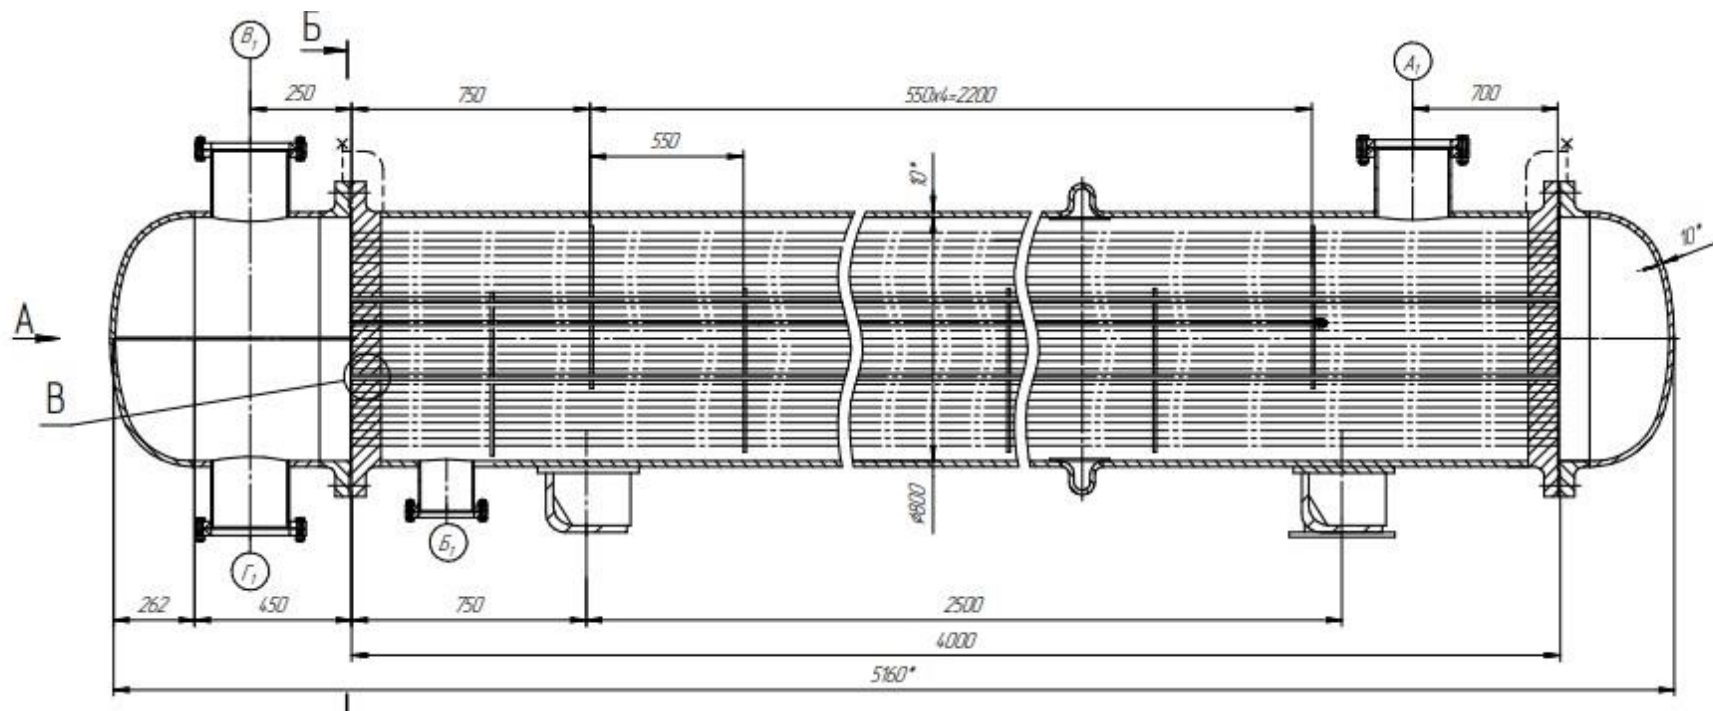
Общий вид конденсатора 1-ой ступени
